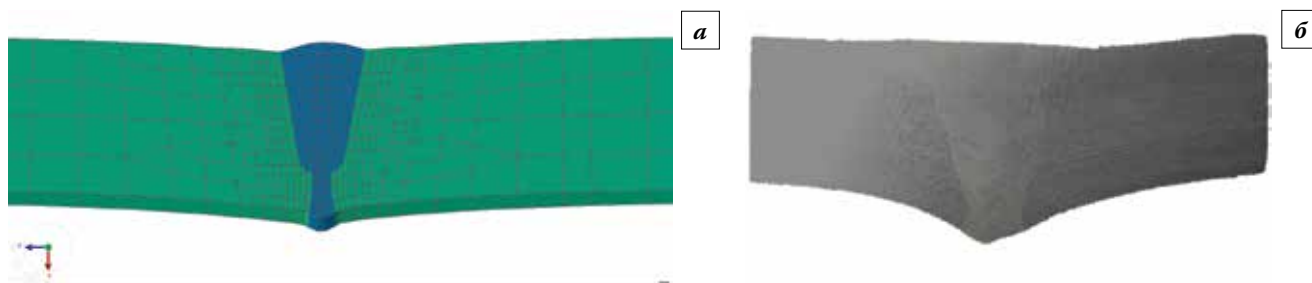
Профиль сечения шва после сварки: а – расчетный; б – экспериментальный
